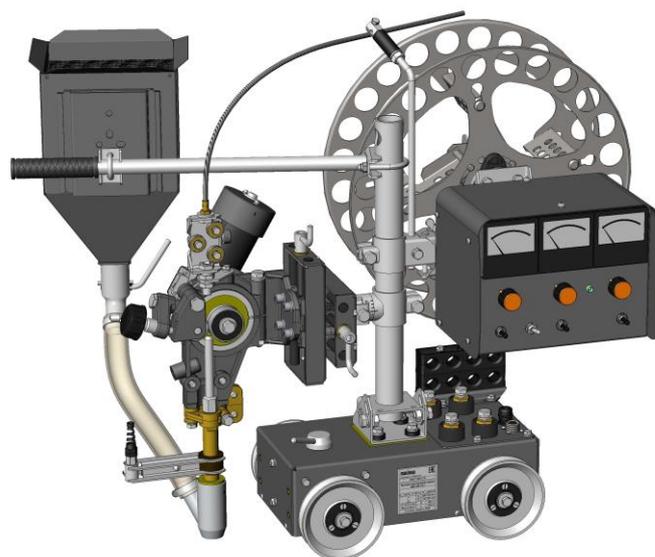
Автомат сварочный АДФ-1000-А исп.03
